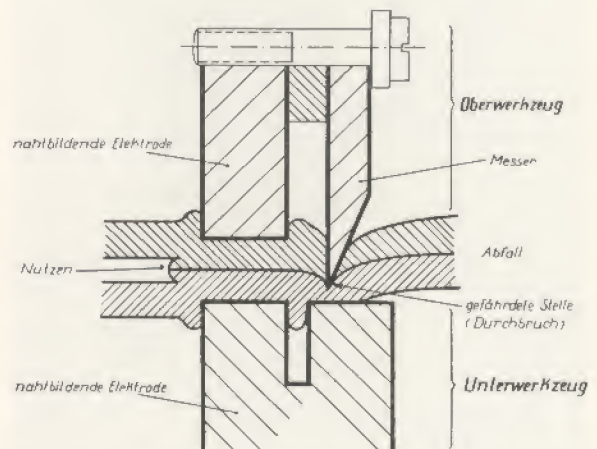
Symmetrisches Schweißwerkzeug mit Schneidmesser
